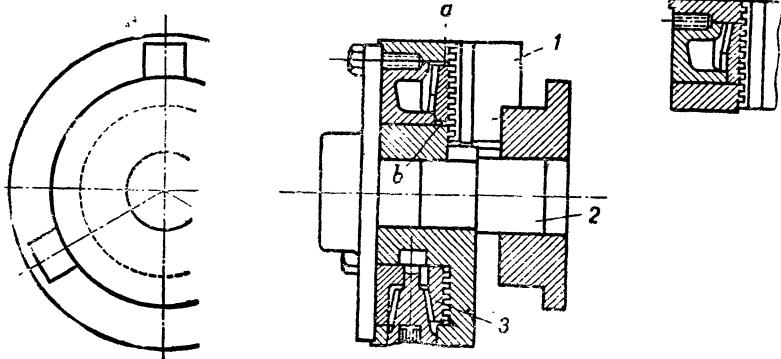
Спиральный патрон с „плавающими“ кулачками.
